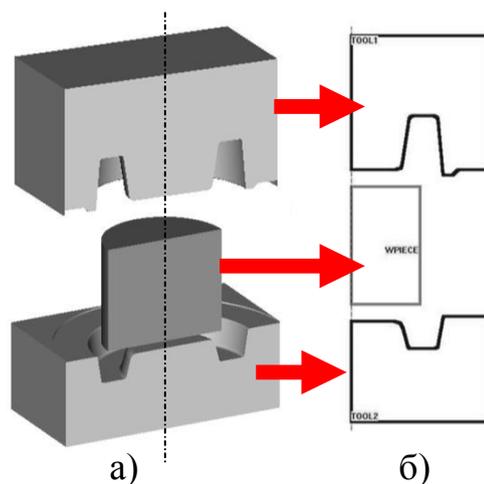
Поперечное сечение заготовки с двумя инструментами (а) и чертеж, подготовленный для моделирования (б) в редакторе QDraft
